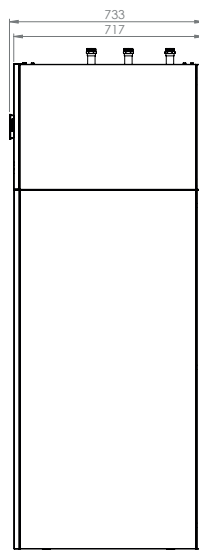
Abmessungen des Onebox Hydraulikschrank - Seitenansicht
